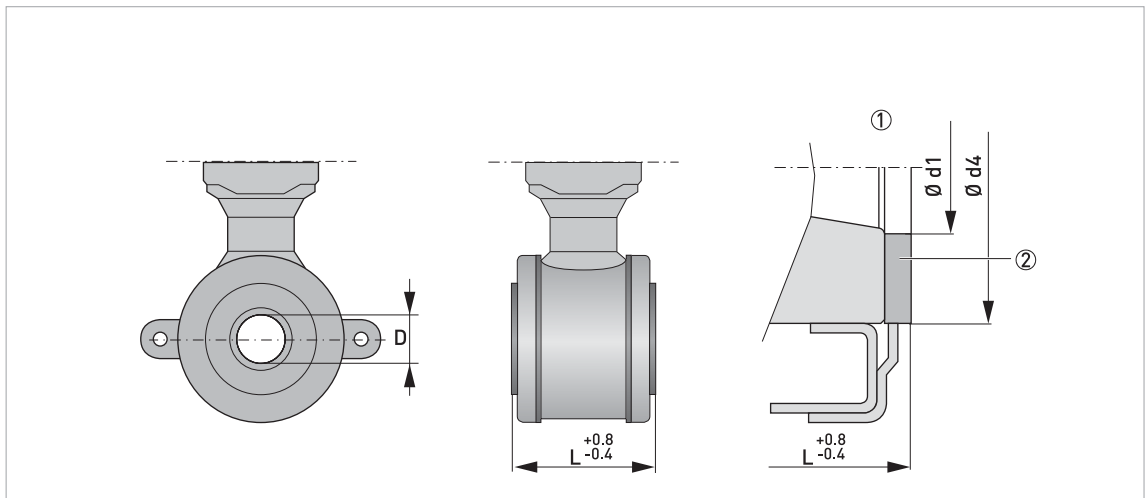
Элементы конструкции DN25...100 / 1...4"
